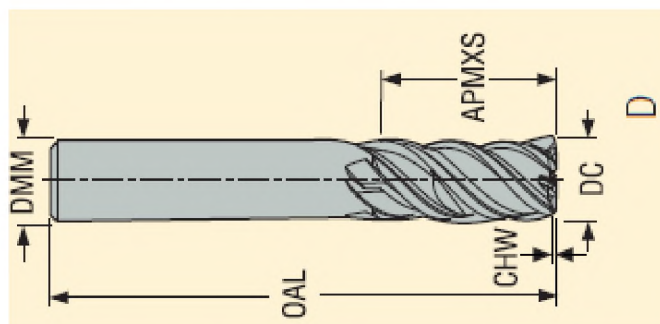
Кінцева фреза Seco 554160Z4.0-SIRON-A [3, с.57]:
